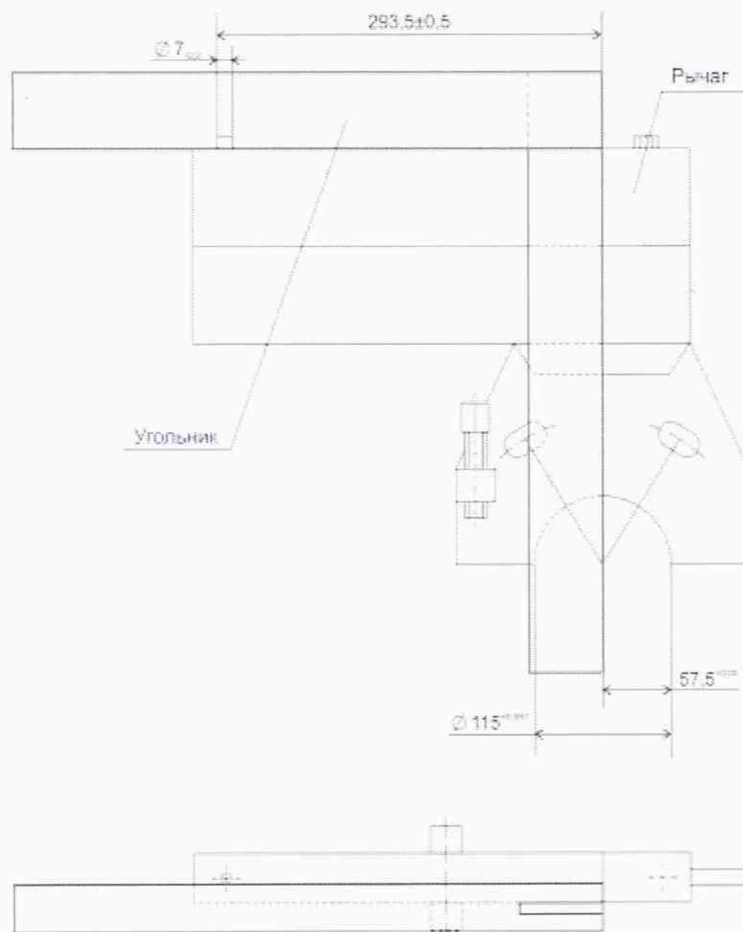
Чертеж рычага М 159.320.00.00
